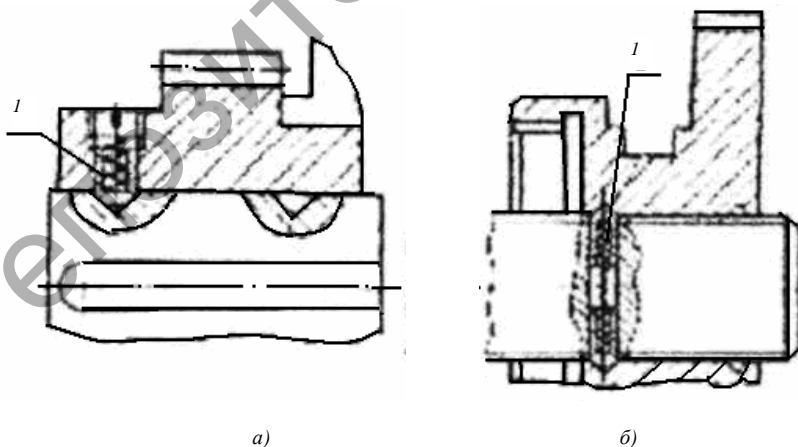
Механизм фиксации блока зубчатых колес
